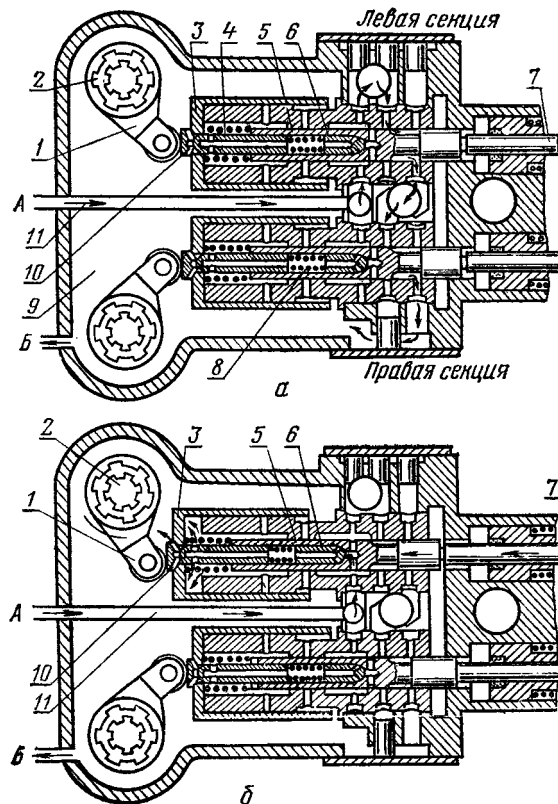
Гидравлический усилитель механизма поворота трактора Т-130:
